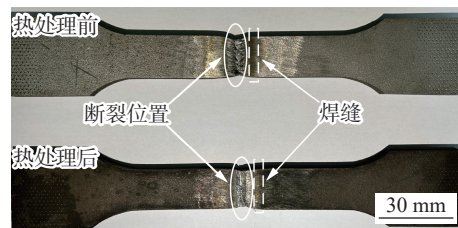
Inconel 600 镍基合金 PA + TIG 接头拉伸试样
